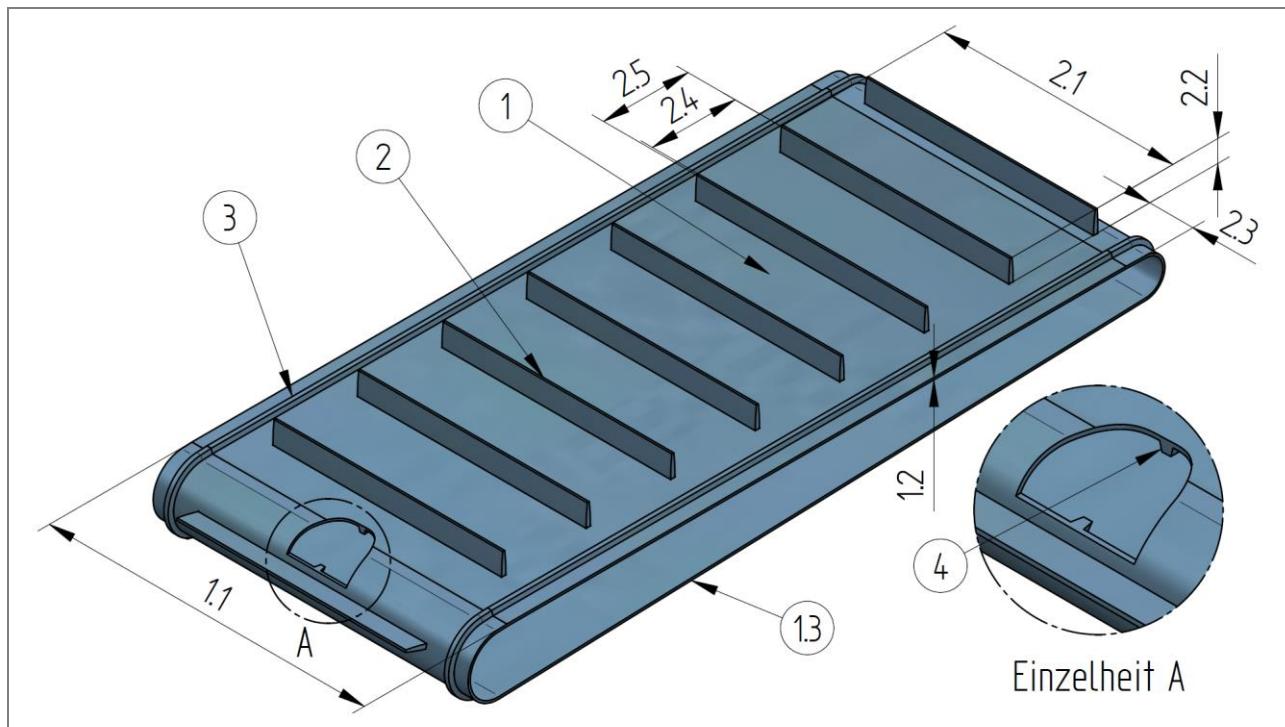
Explosivní náhled rovného pásového dopravníku (příklad)
